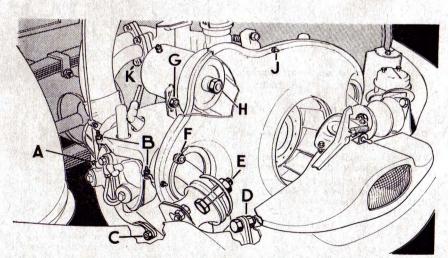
Fig. D. — Dépose d'un cylindre sur moteur « Aérodyne »
